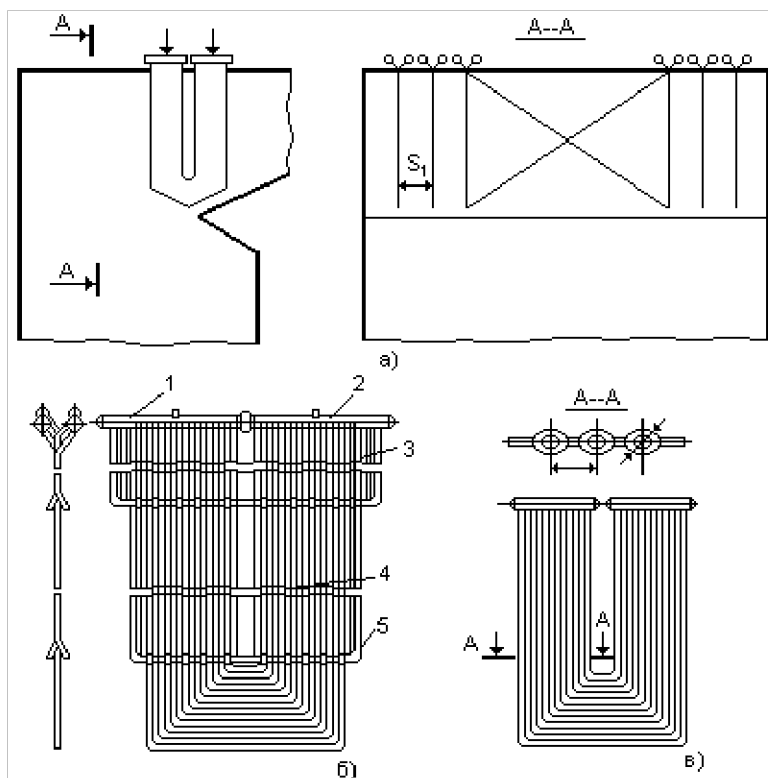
Расположение и конструкции ширмового пароперегревателя: а - расположение ширм на выходе из топки; б - обвязка труб ширмы; в - вид цельносварной ширмы;
